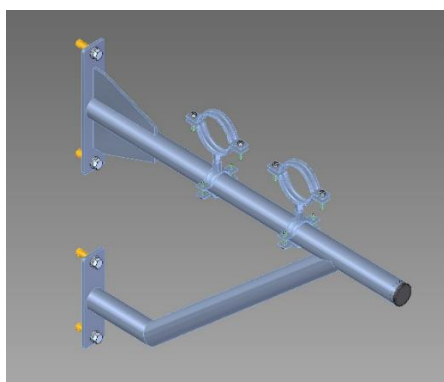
Strutture a sostegno delle tubazioni sulla parete ovest (Solid Edge)
